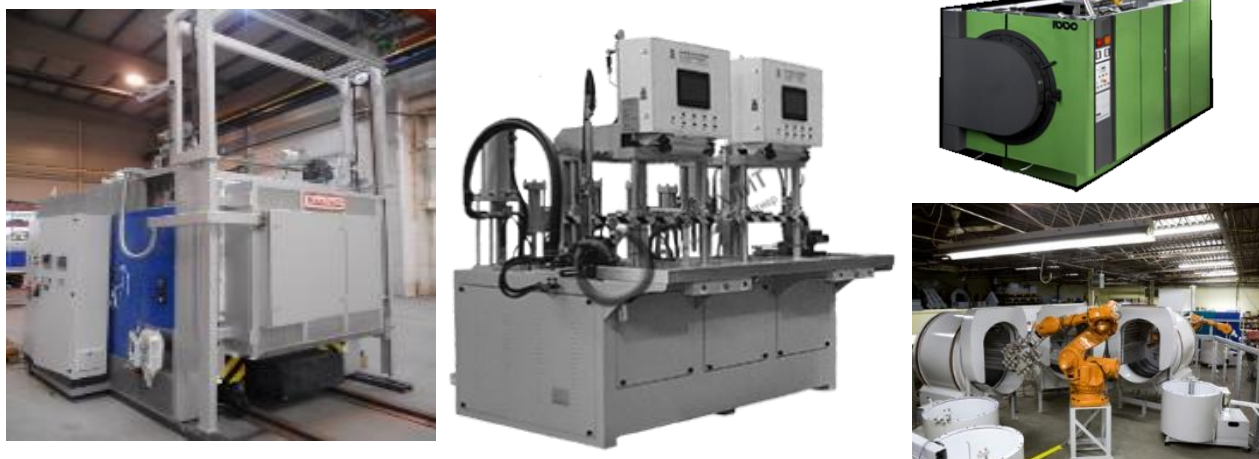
Новое оборудование: печь, роботизированный комплекс нанесения огнеупорного покрытия, шприц-машина, бойлерклав.
